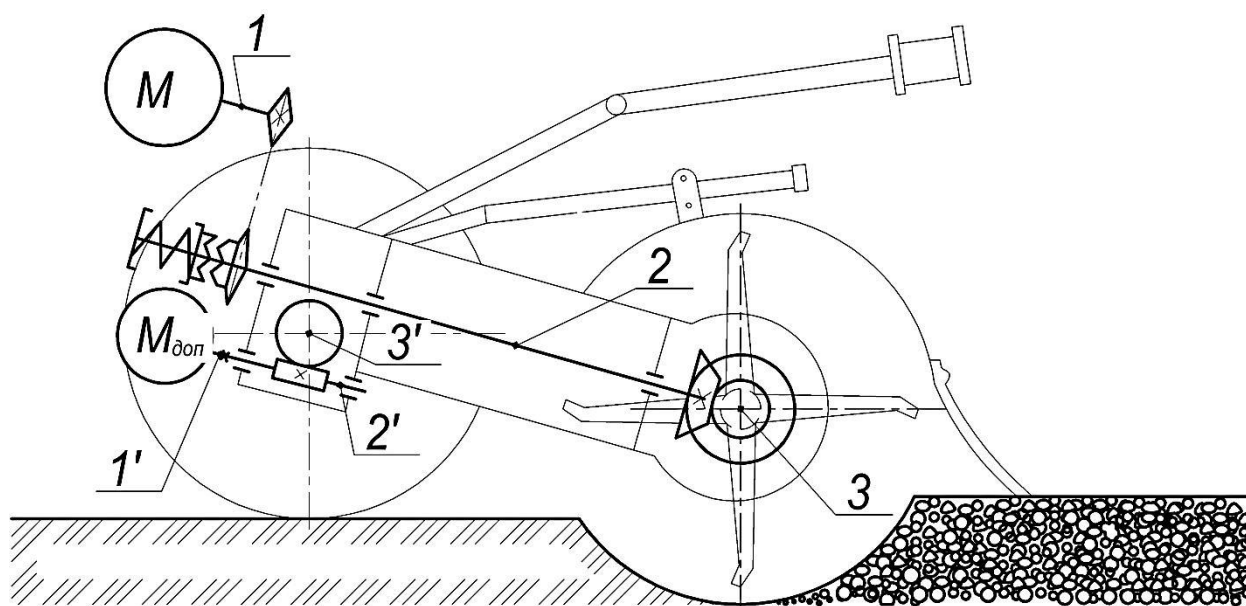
Кинематическая схема малогобаритной фрезы.
